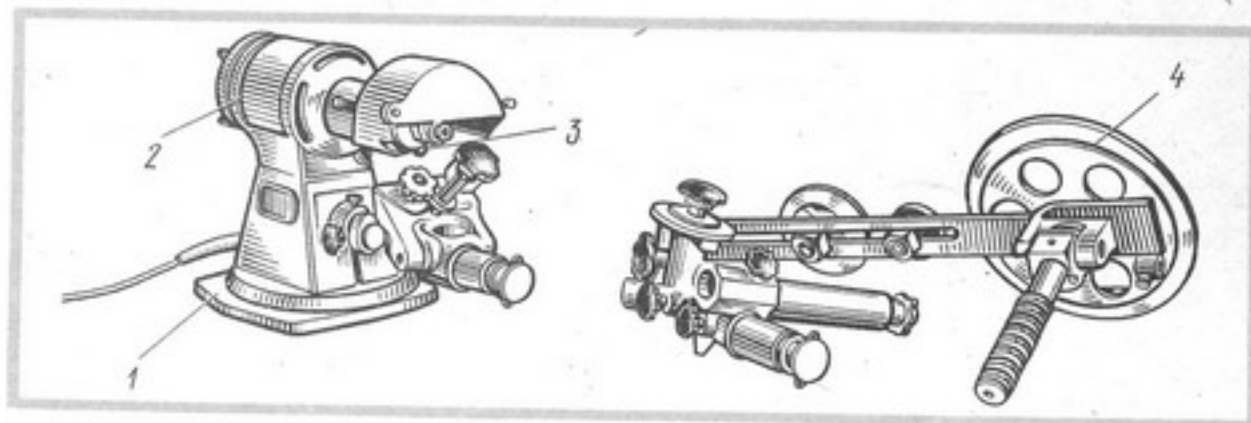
Станок ИЭ-9703 для заточки режущего инструмента:
